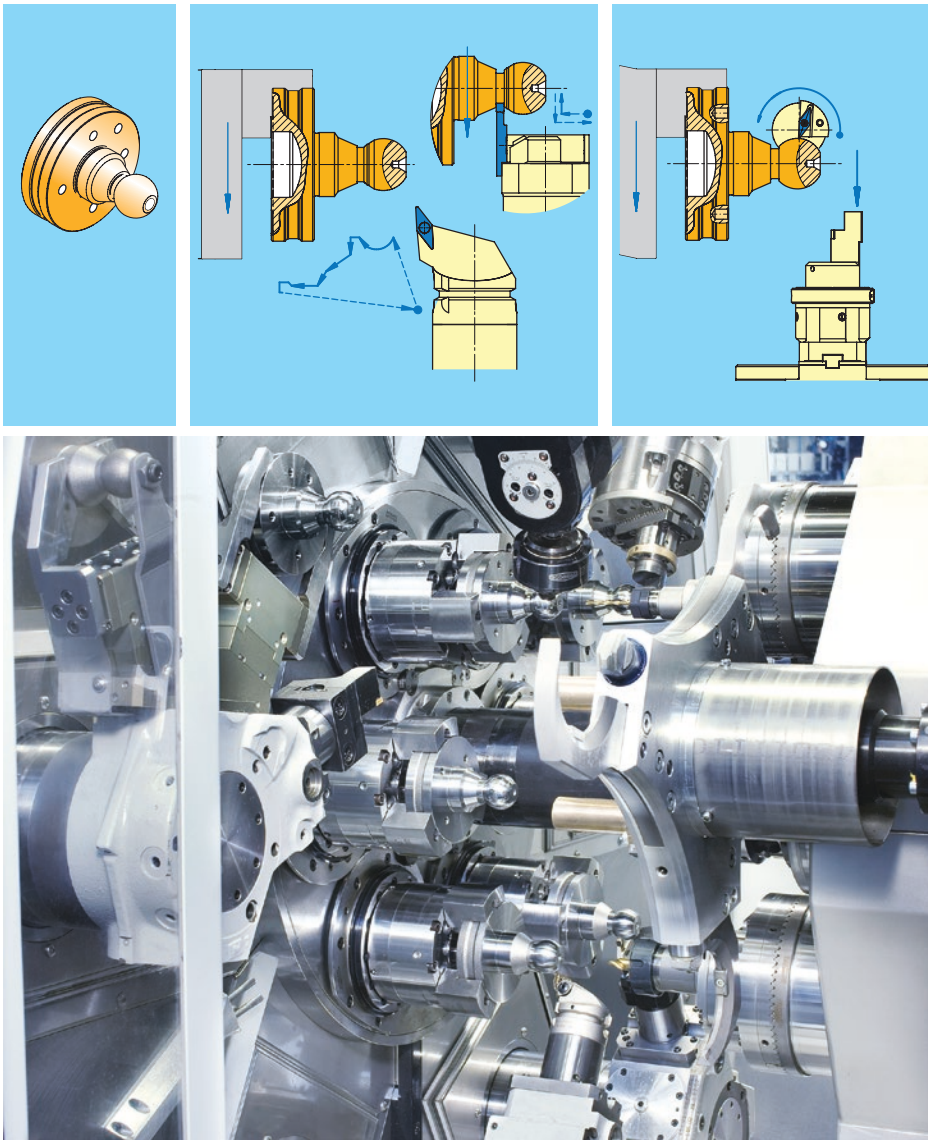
Beispielwerkstück und Verfahrensvarianten des Kugeldrehens; unten eine CNC-gesteuerte Kugeldrehmaschine. [Quelle: Schütte]
